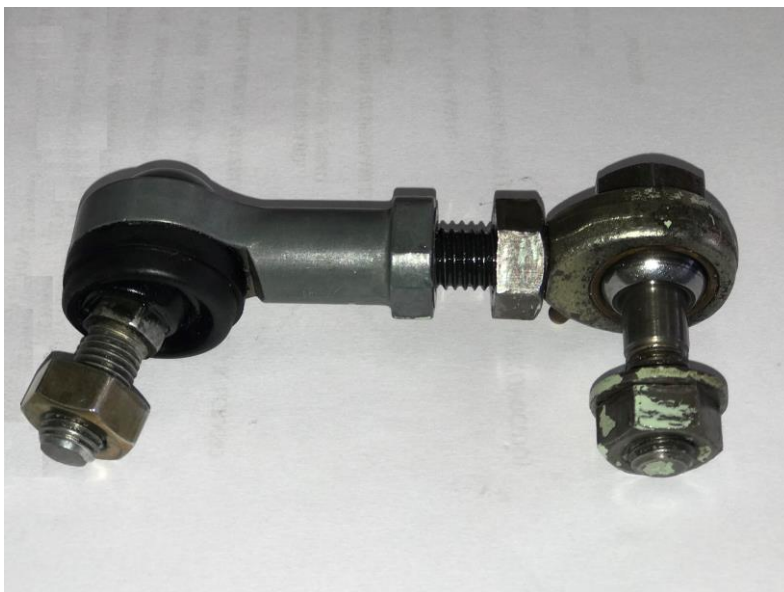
Unión articulada del motor principal de babor, en sus tres partes ensambladas
